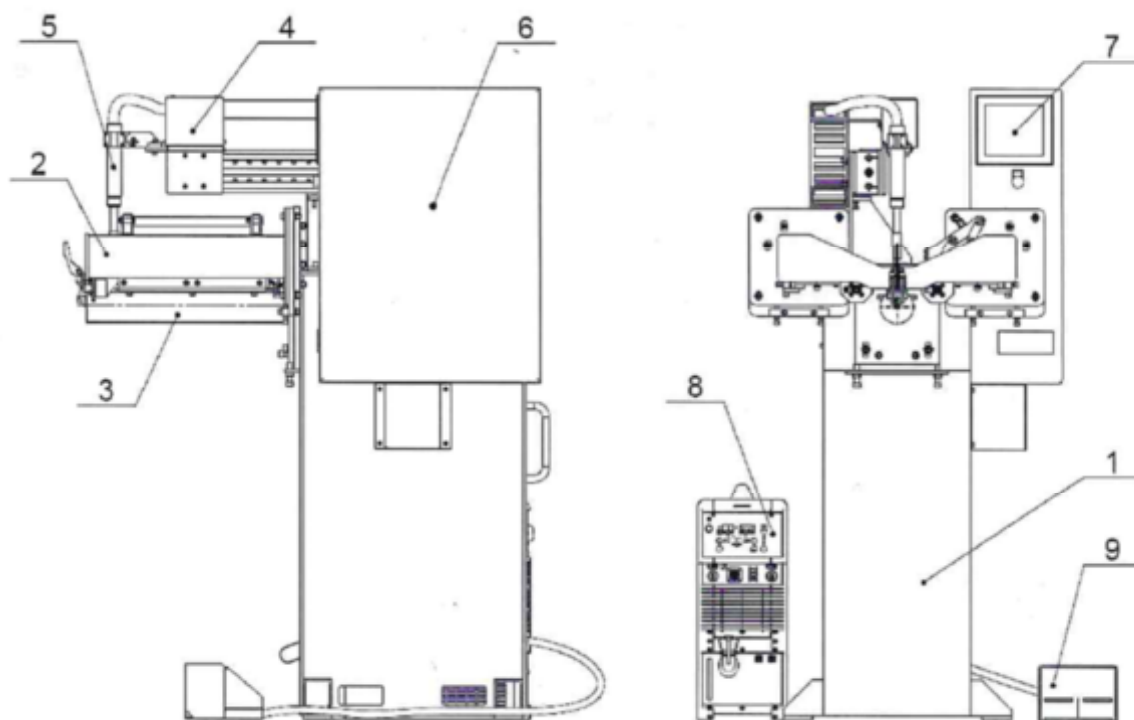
Сварочный комплекс ИРС-МСУ-400-002
